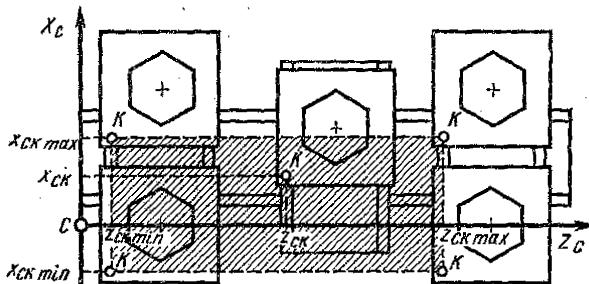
Диапазон перемещений базовой точки суппорта токарного станка
